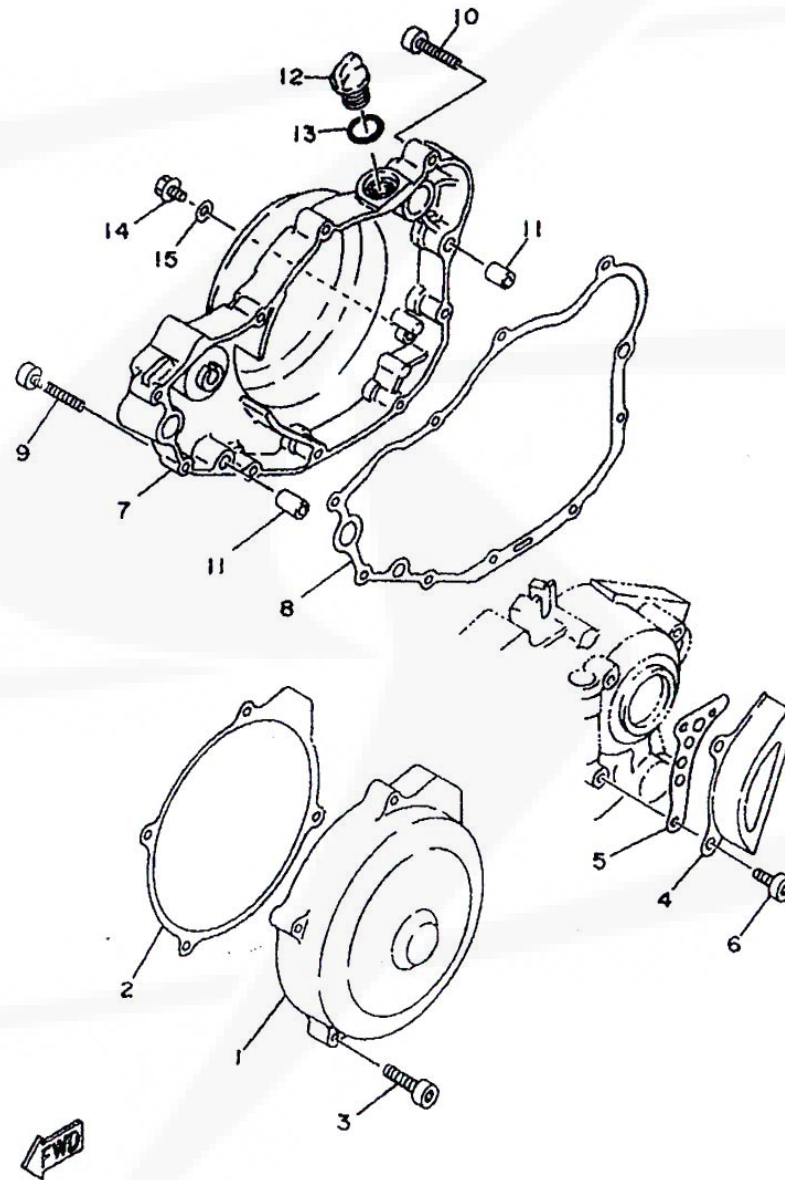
COUVRE CARTERS / CRANKCASE COVER / CUBRE CÁRTER
